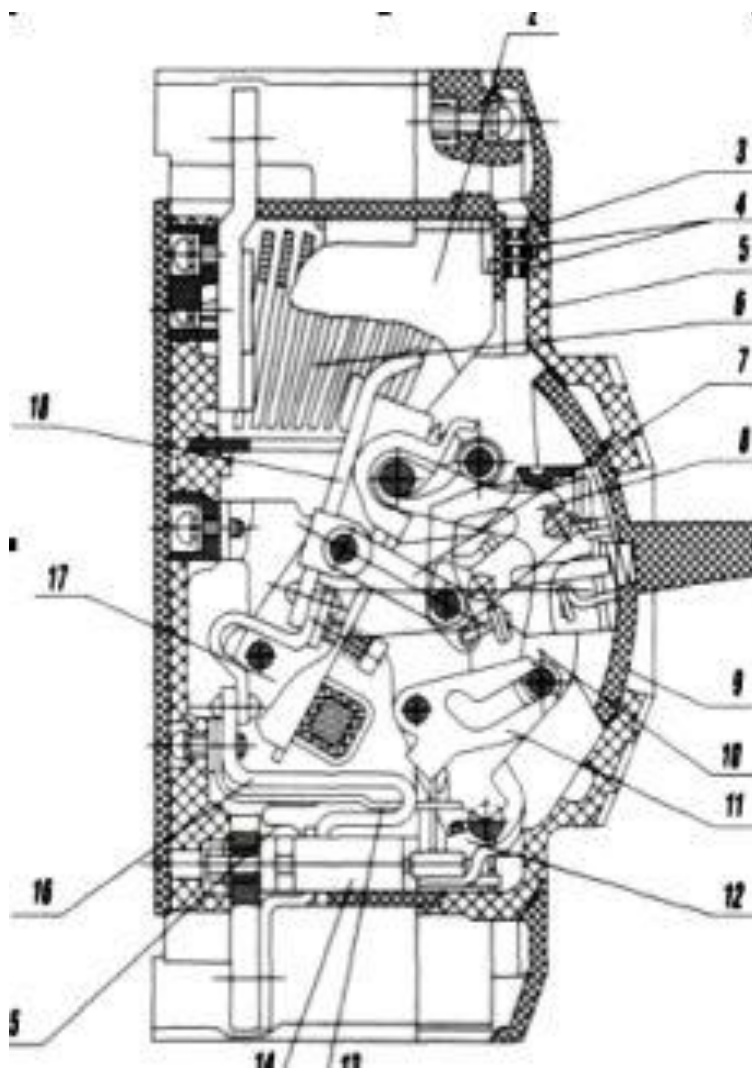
Автоматический выключатель, серия ВА 04-36 (устройство выключателя): 1- основание, 2- камера дугогасительная, 3, 4-пластины искрогасительные, 5-крышка, 6-пластины. 7-звено, 8-звено, 9-рукоятка, 10-рычаг опорный, 11-защелка, 12- рейка отключающая, 13- пластина термобиметаллическая, 14-расцепитель элетромагнитный, 15 -проводник гибкий, 16-токопровод, 17- контактодержатель, 18-контакты подвижные
